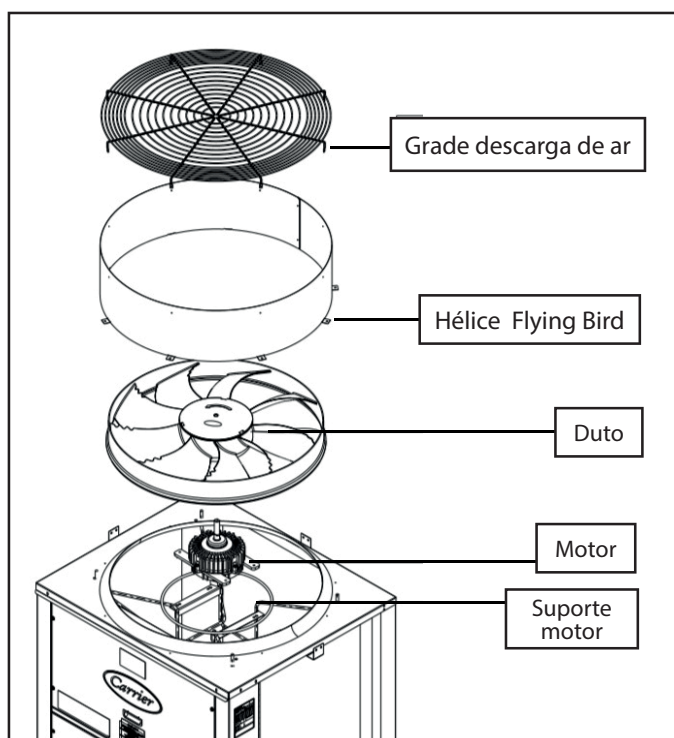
Vista explodida conjunto ventilador das unidades 30EX/30EV e Hélice Flying Bird
